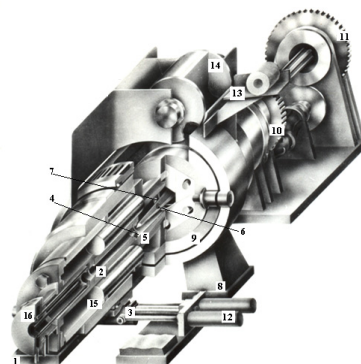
Конструкция горизонтальной прессовой установки обратного прессования с конической оправкой: 1 – станина пресса; 2 – пресс-штемпель; 3 – привод механизма затвора контейнера; 4 – матрица; 5 – контейнер; 6 – игла независимой прошивной системы; 7 – затвор контейнера; 8 – опора станины; 9 – блок рабочих цилиндров; 10 – гидромеханический привод перемещения иглы; 11 – гидромеханический привод поворота иглы; 12 – гидроцилиндры привода затвора контейнера; 13 – стол подачи литых заготовок; 14 – загрузочное устройство; 15 – блок возвратных цилиндров; 16 – устройство охлаждения
